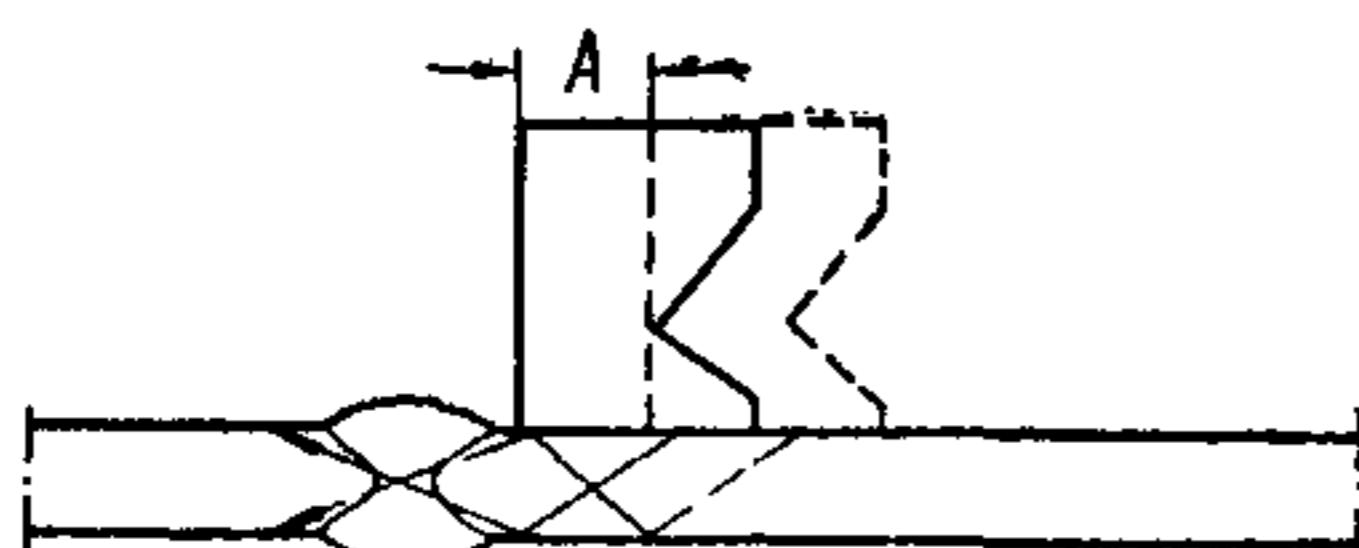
Определение зоны перемещения искателя при ультразвуковом контроле сварного стыка толщиной стенки до 20 мм
